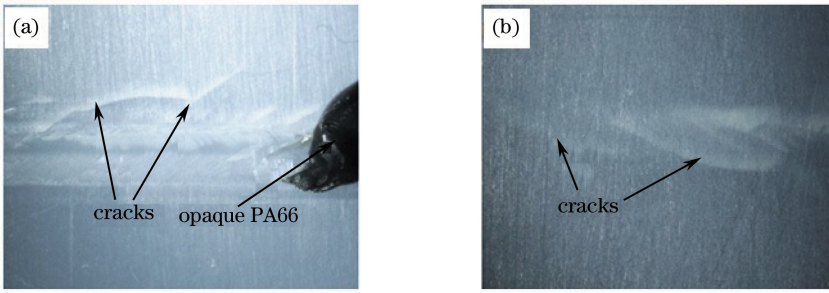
拉伸断裂后 PA66 透光层试样上的裂纹形貌。(a) 焊接界面；(b) 外表面
